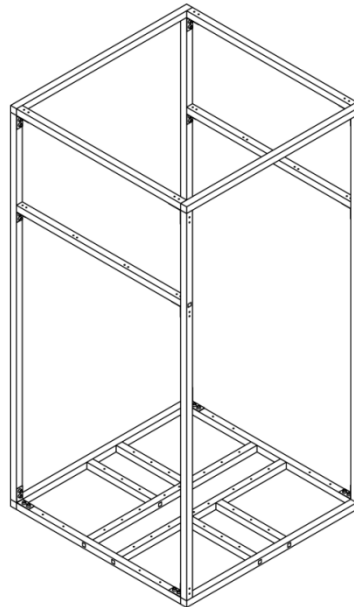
1: Vista isométrica del ensamblaje de la estructura. Fuente: Elaboración propia.
